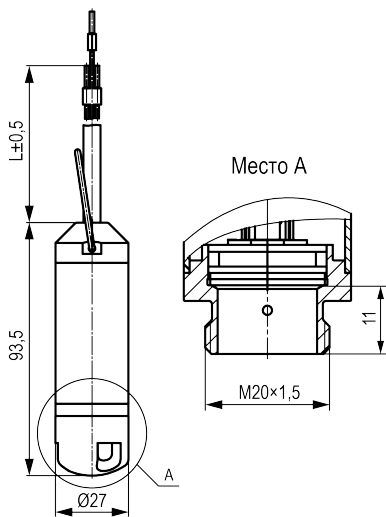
Габаритные и присоединительные размеры ПД100И-167
